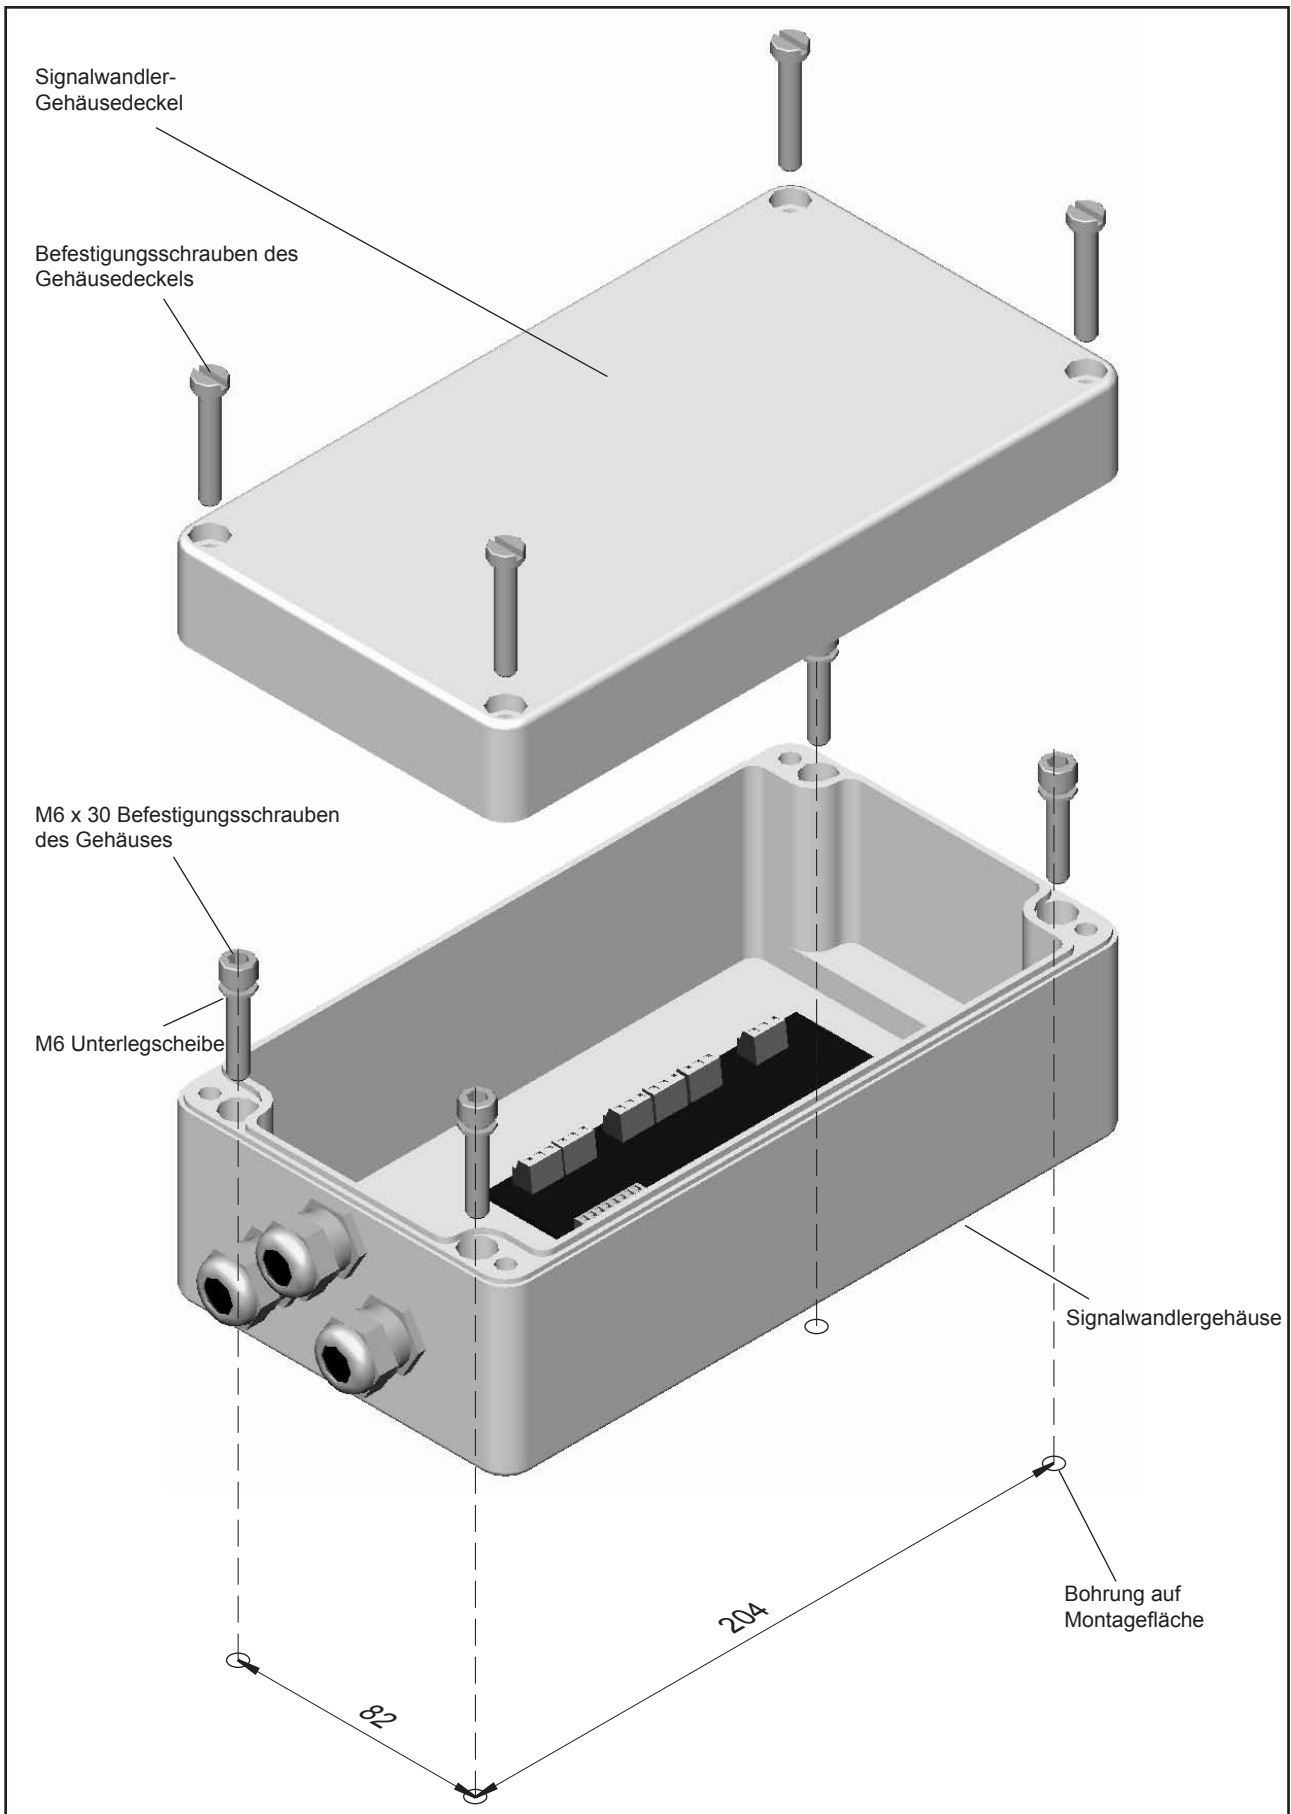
Montage eines CST 113 mit Aluminiumgehäuse
